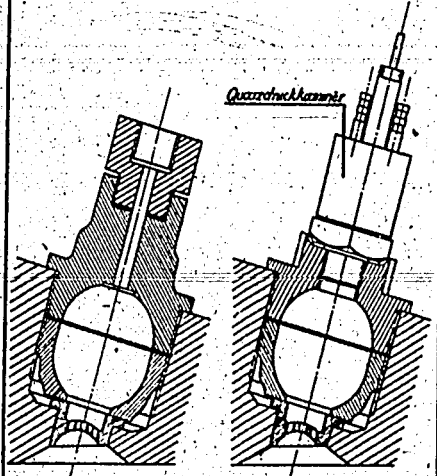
Ansicht mit Druckbohrung Abb. 12 Unmittelbarer Anschluß
